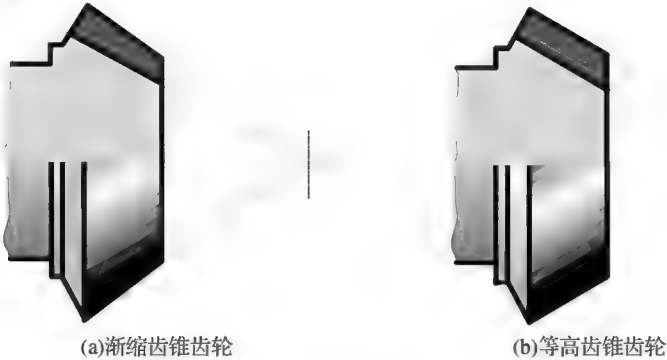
渐缩齿锥齿轮和等高齿锥齿轮
